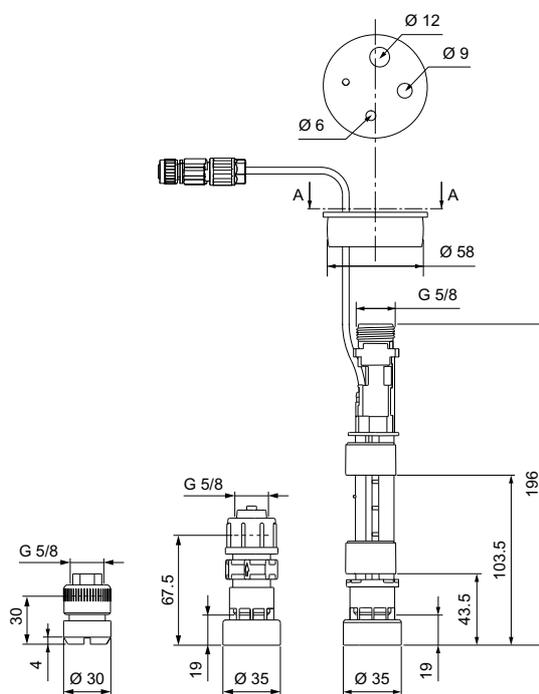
Gauche : Clapet de pied inox ; centre et droite : clapet de pied PE ou PVDF, dimensions
